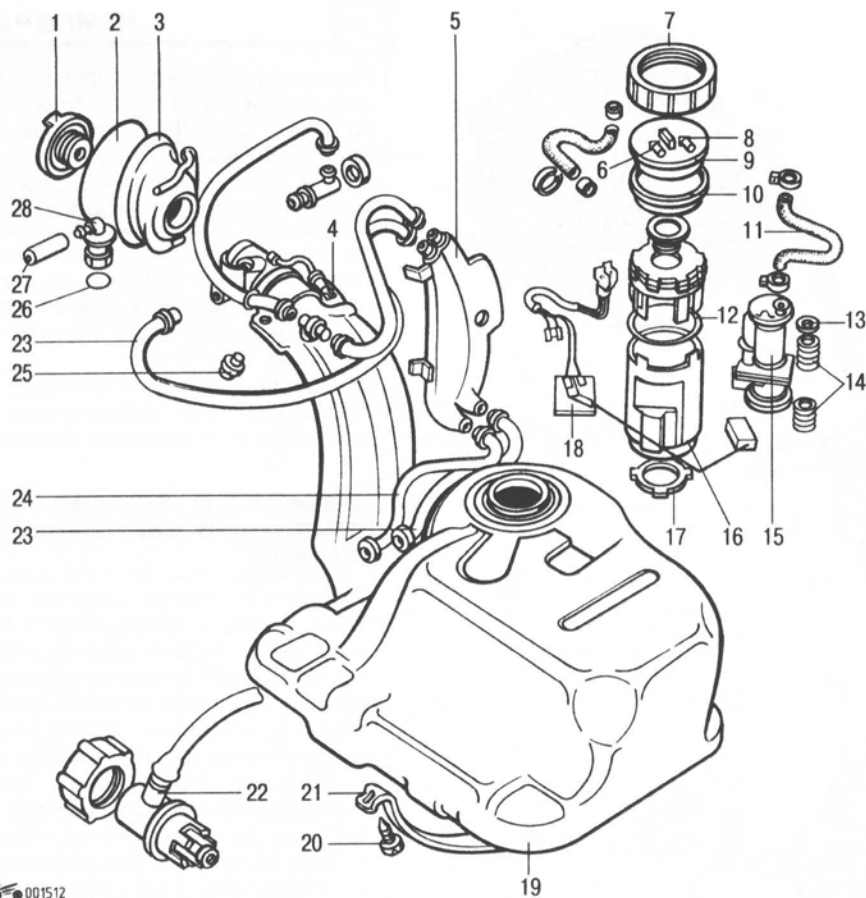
Топливный бак и топливный насос автомобилей с двигателем SOHC: 1 – крышка наливной горловины; 2, 17 – стопорные кольца; 3 – резиновый уплотнитель; 4 – контакт провода заземления; 5 – расширительный бачок; 6 – патрубок напорной магистрали; 7 – фланцевая гайка; 8 – патрубок возвратной магистрали; 9 – крышка; 10, 12, 26 – уплотнения; 11 – шланг; 13 – шайба; 14 – резиновые демпферы; 15 – топливный насос; 16 – кожух топливного насоса; 18 – датчик уровня топлива; 19 – топливный бак; 20, 25 – болты; 21 – стальной хомут крепления топливного бака; 22 – клапан вентиляции; 23 – трубка сапуна (универсал); 24 – трубка сапуна; 27 – шланг к угольному адсорберу; 28 – клапан
